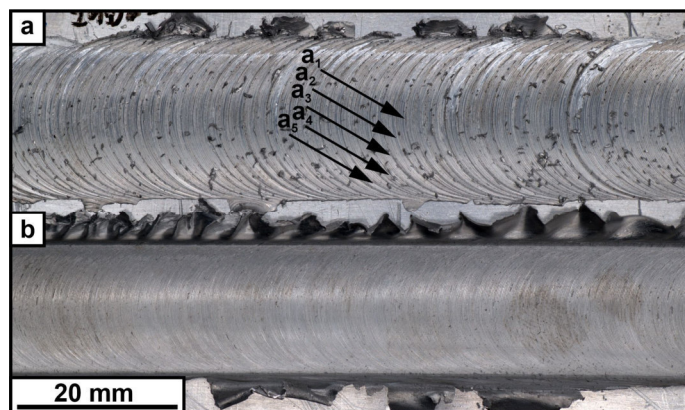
Внешний вид поверхности зоны обработки инструментом с пином квадратной (а) и винтовой (b) формы
